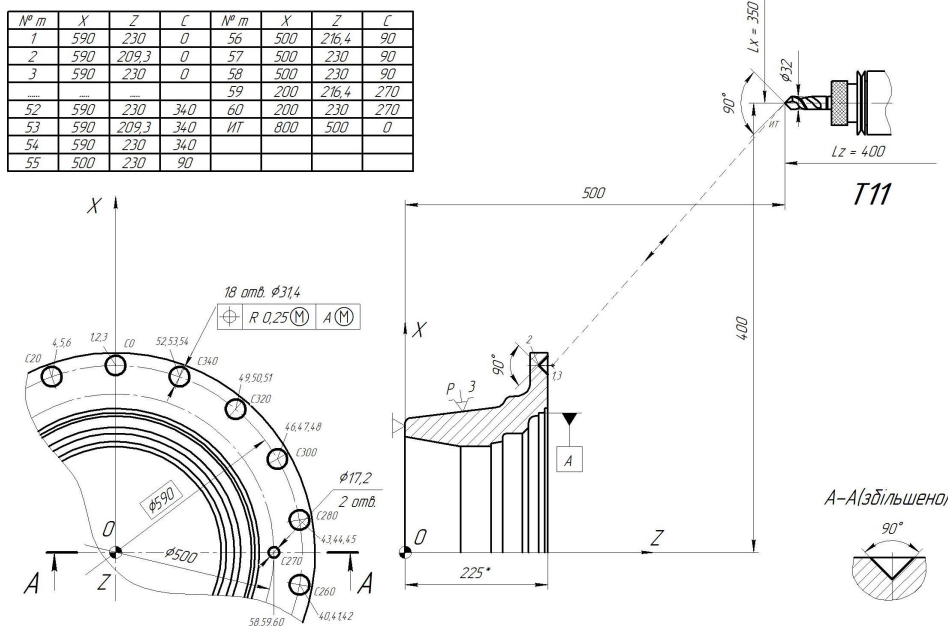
Установ А, перехід 3: схема обробки деталі та координатне розташування інструмента
